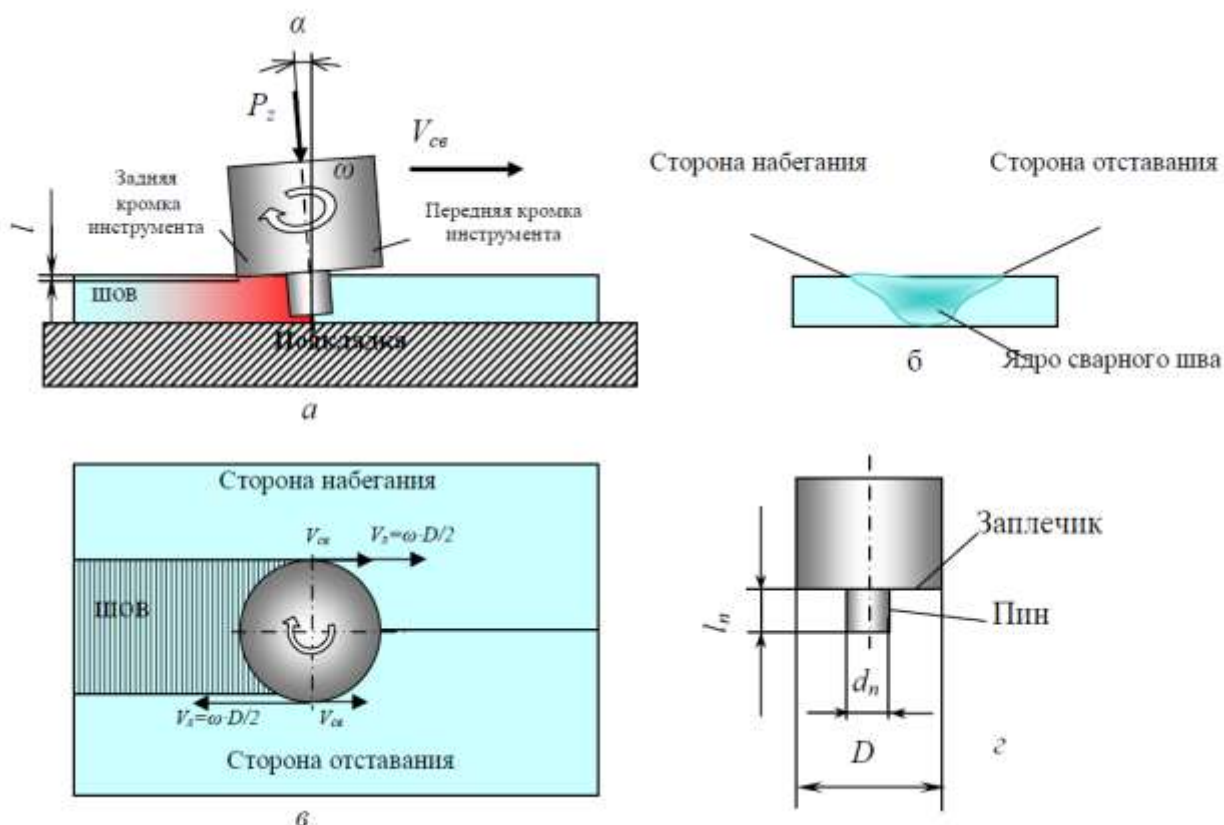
Сущность сварки трением с перемешиванием:
